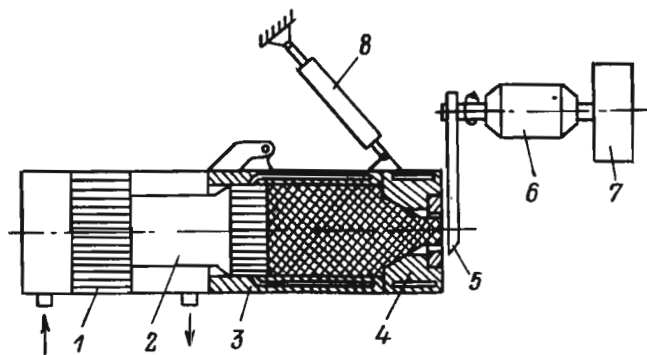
Схема предформователя заготовок типа «Барвелл»:
